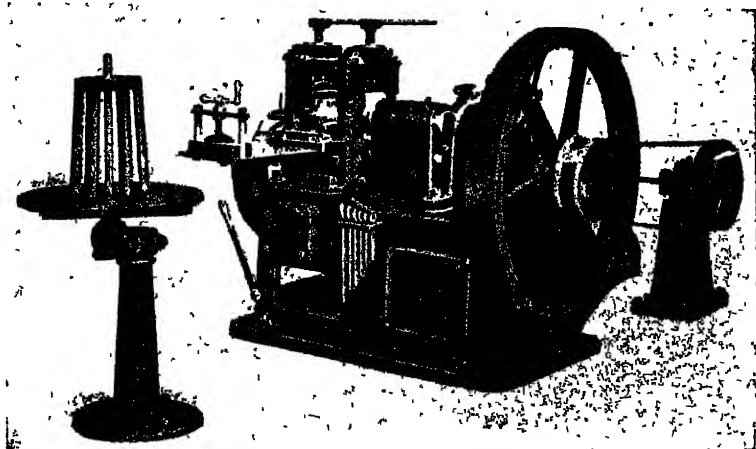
Laminoir pour la fabrication du papier d'aluminium.
